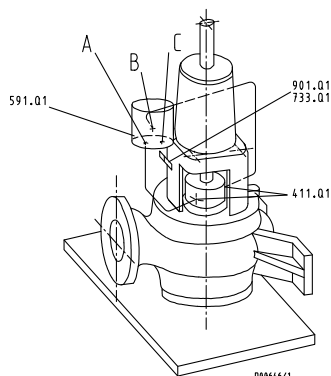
Крепление бачка затворной жидкости — вертикальная установка
